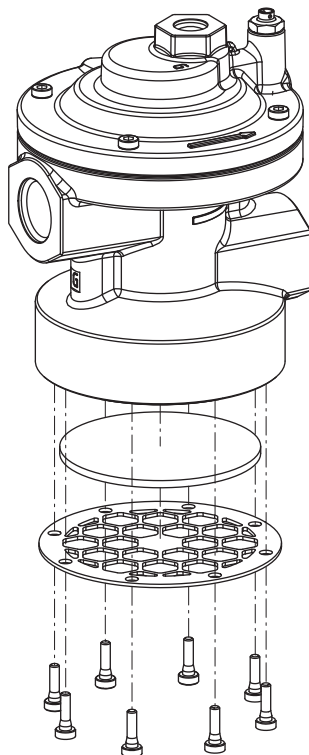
Монтаж типа 3755-1: шумопоглощающий фильтрующий диск из порошкового полиэтилена
